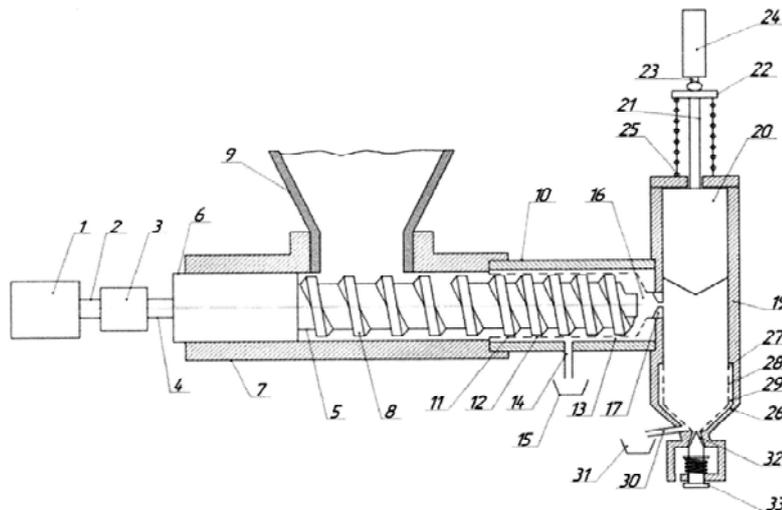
Кинематическая схема установки для холодного прессования ядра кедрового ореха
